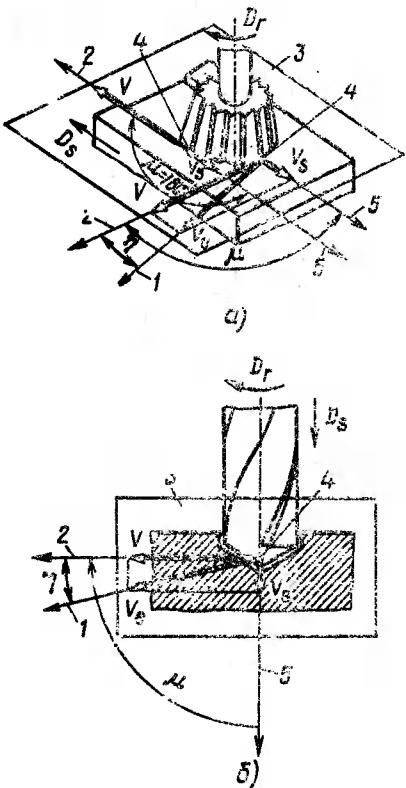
Элементы движений в процессе резания при фрезеровании концевой угловой фрезой (а) и при сверлении (б):
